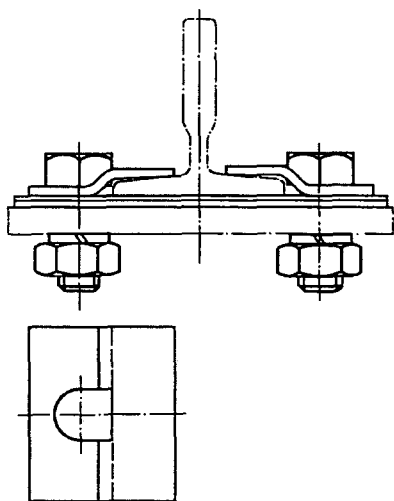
Крепление направляющей с помощью штампованных прижимов (Wittur Aufzugteile GmbH)
